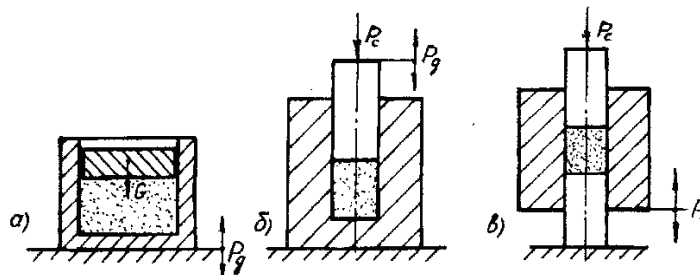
Схеми пресування заготовок у закритій прес формі при вібруванні контейнера (а), пуансона (б) та матриці (в)
